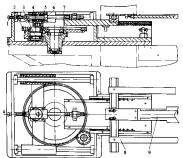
行星齿轮传动纵向送料机构 1一定位挡块; 2一转臂; 3一行星齿轮; 4一模心轮; 5一弹簧装置; 6一槽形导轨; 7一中心齿轮; 8一夹板; 9一推板
